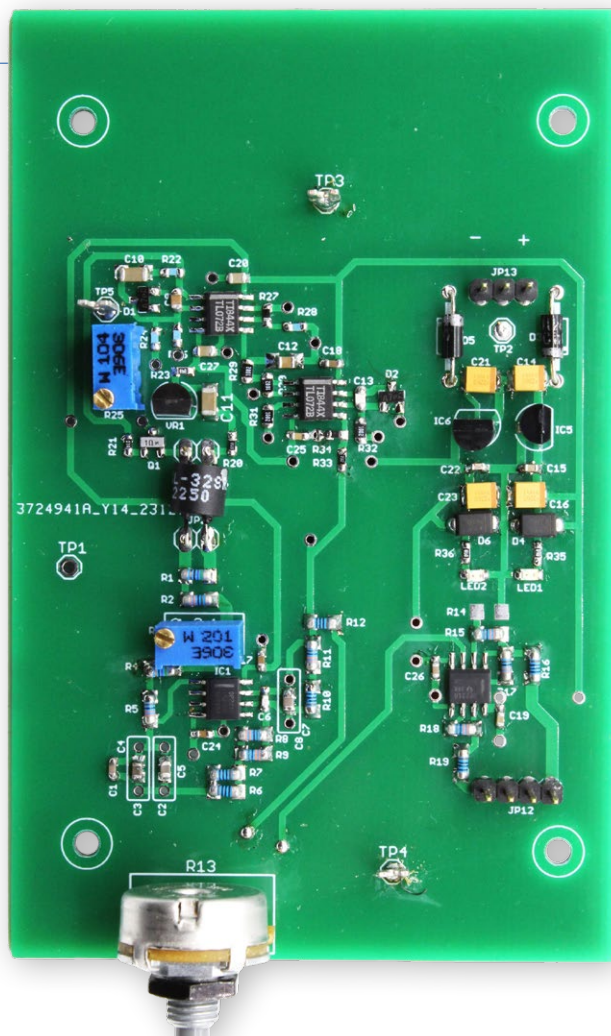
Le circuit imprimé entièrement assemblé de mon prototype.
